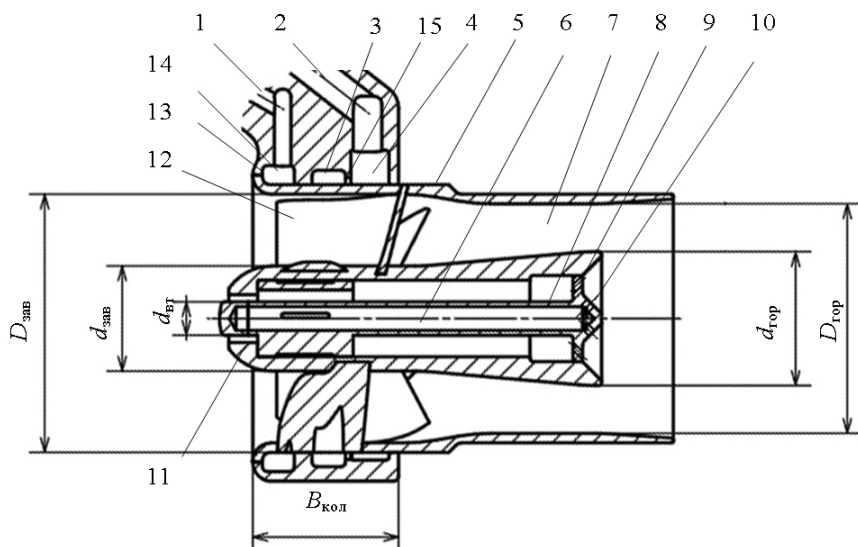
Конструктивная схема горелочного устройства МКС ГТД ВПТЦ НК-38СТ
